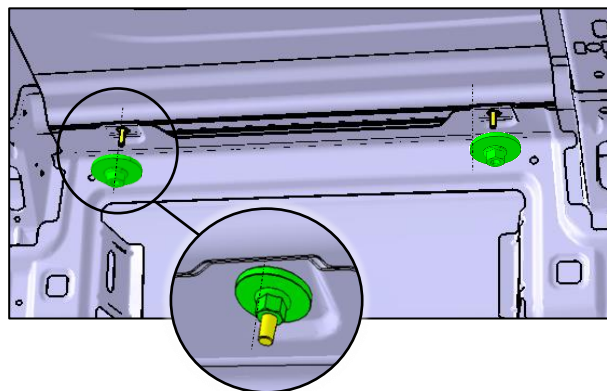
Vista interior de puntos de atornillado en la zona del techo
